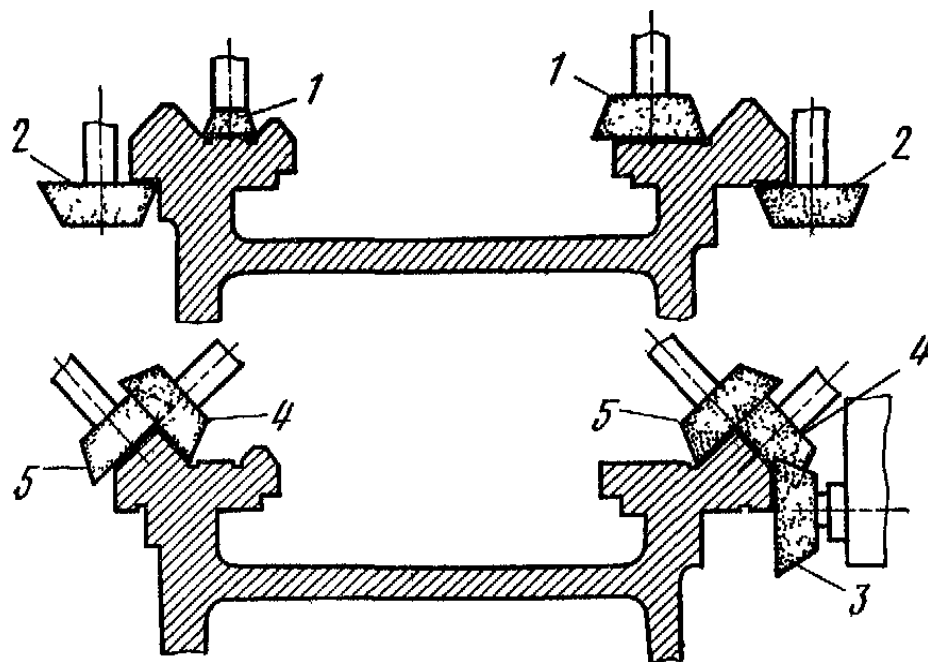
Схема шлифования направляющих станины станка чашечными кругами
